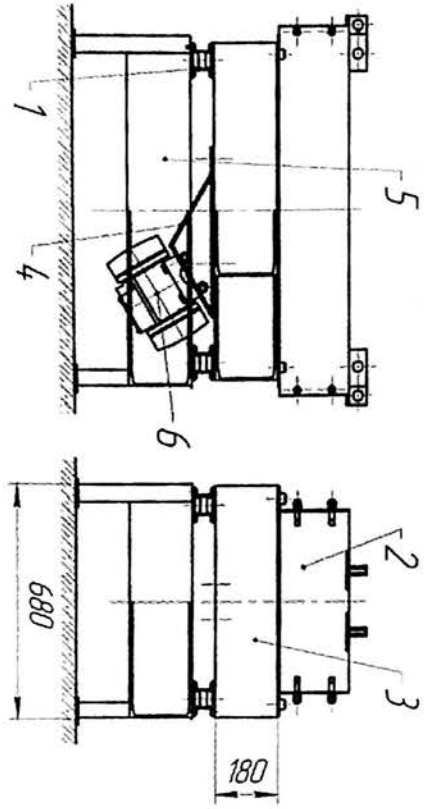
Віброустановка для формування малогабаритних бетонних і залізобетонних виробів
